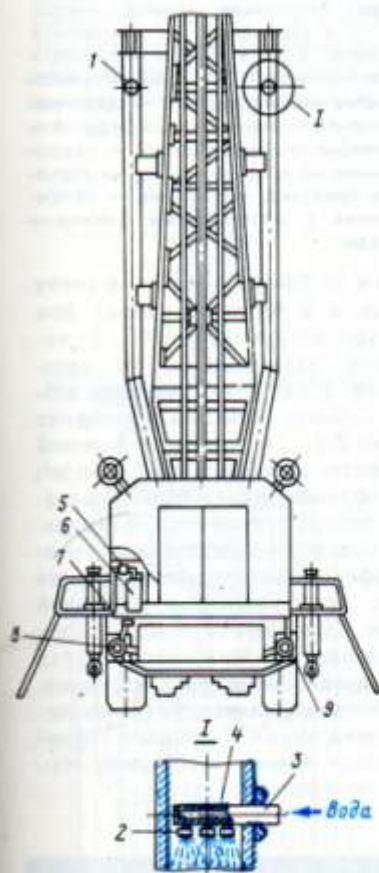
Схема расположения установки ПГПУ на станке СБТМ-20:
